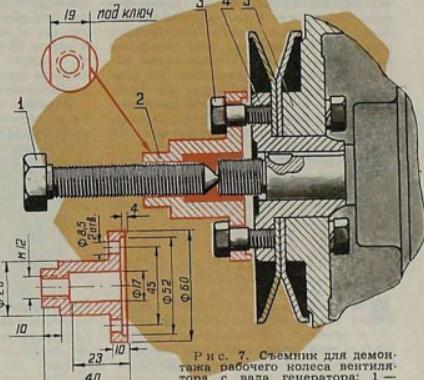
Съемник для демонтажа рабочего колеса вентилятора с вала генератора: 1 — болт M12×60; 2 — корпус съемника; 3 — болт M8×15; 4 — ступица рабочего колеса вентилятора; 5 — рабочее колесо вентилятора.
